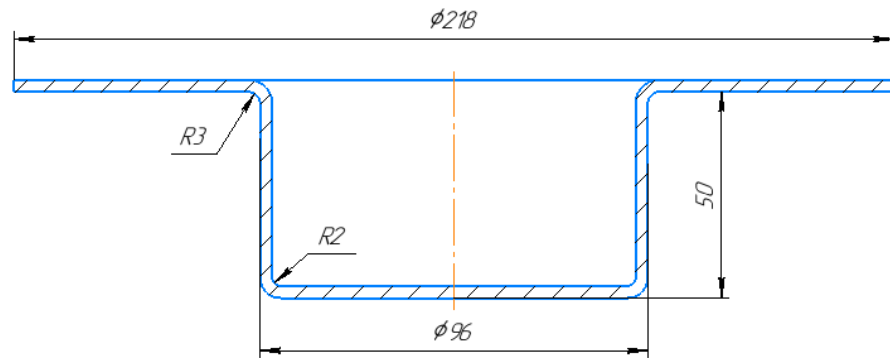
Эскиз заготовки с широким фланцем
